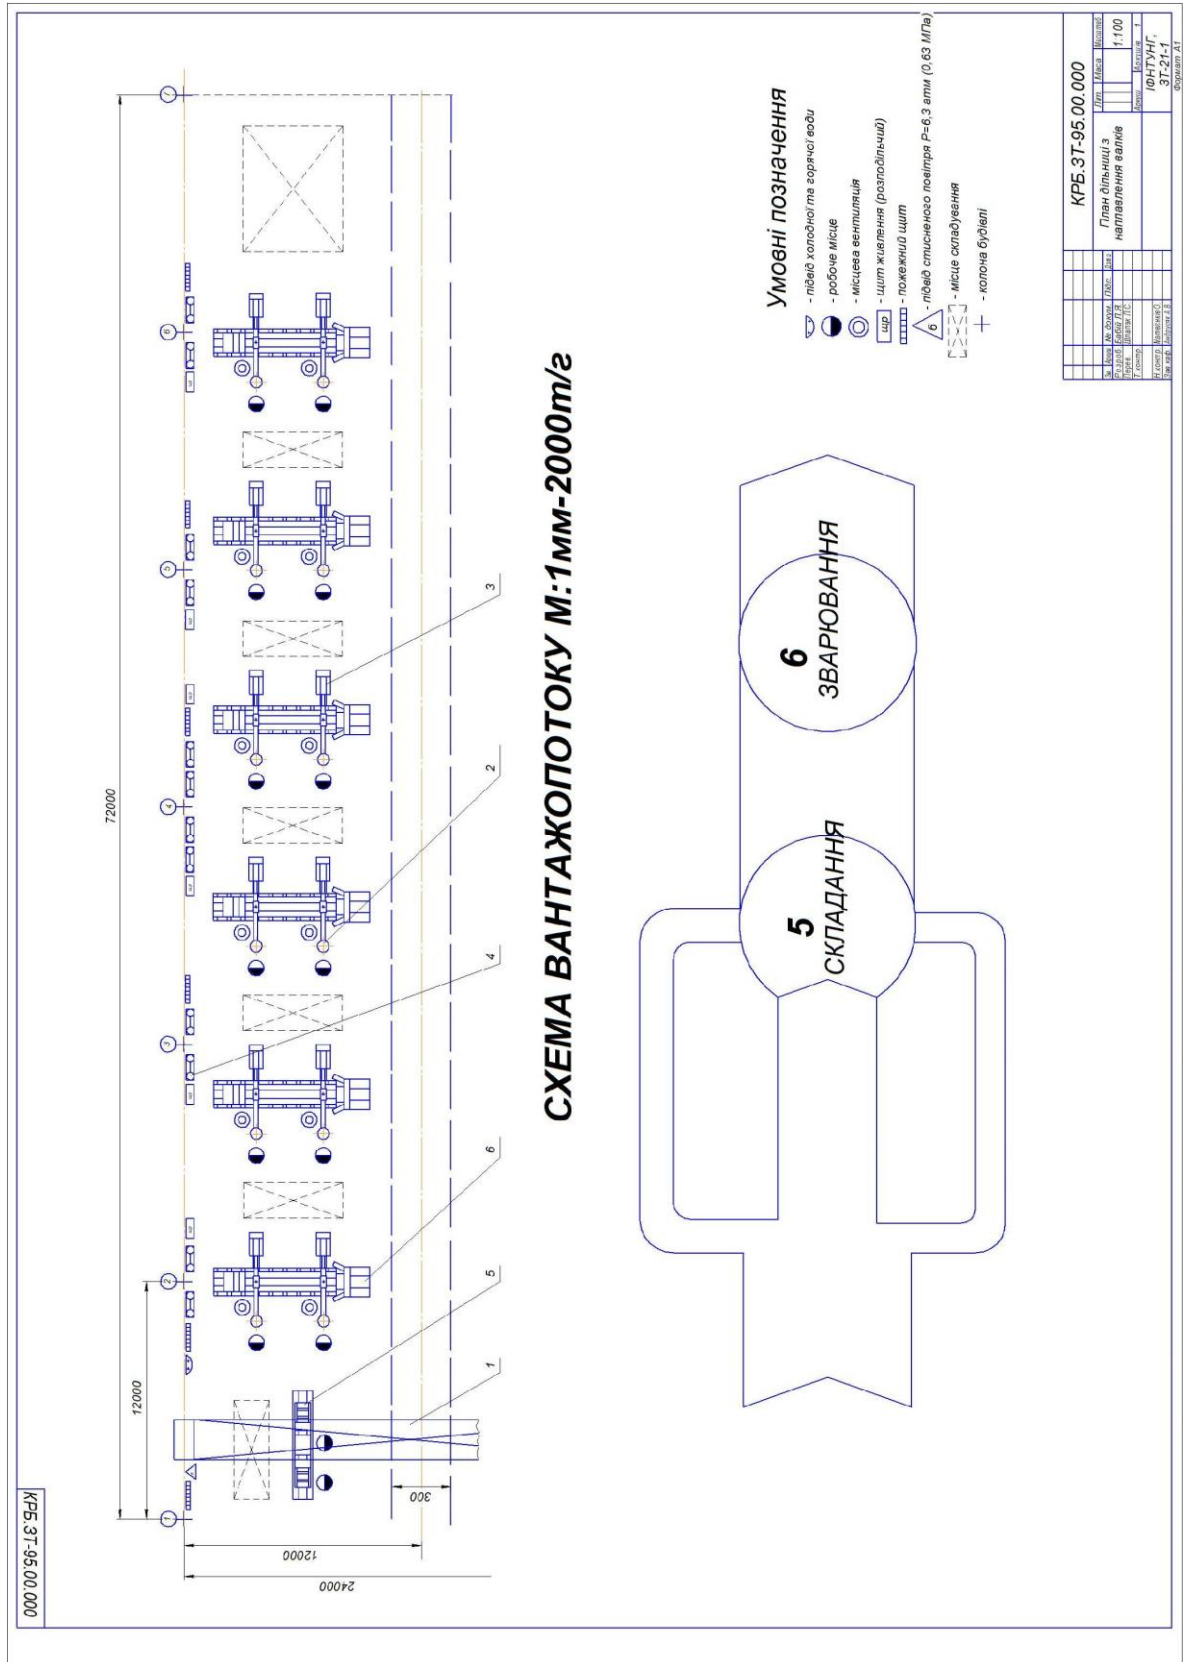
План цеху для наплавлення валка прокатного стану
